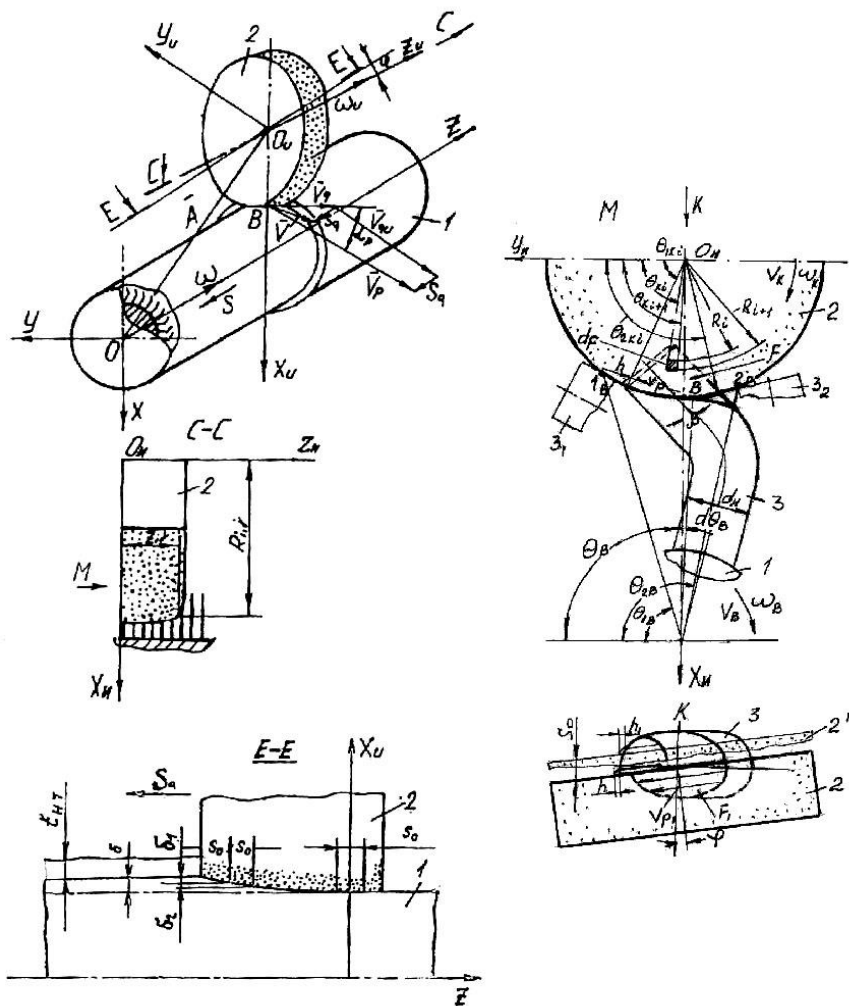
Схема шлифования игольчатой поверхности со скрещивающимися осями круга и рабочего валика
